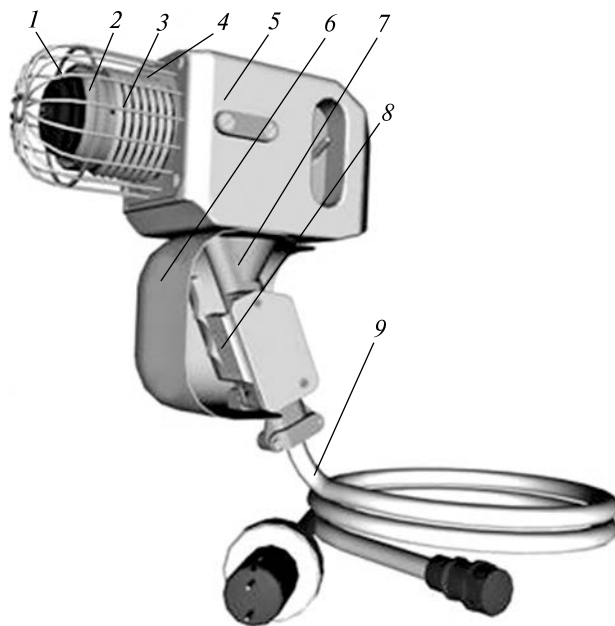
Загальний вигляд ручного електронно-променевого інструмента для зварювання в умовах космосу [12]: 1 — анодний блок, 2 — катодний блок, 3 — радіатор охолодження, 4 — захисна сітка, 5 — корпус катодного блока, 6 — гарда, 7 — рукоятка, 8 — гашетка, 9 — кабель з високовольтним з'єднувачем
